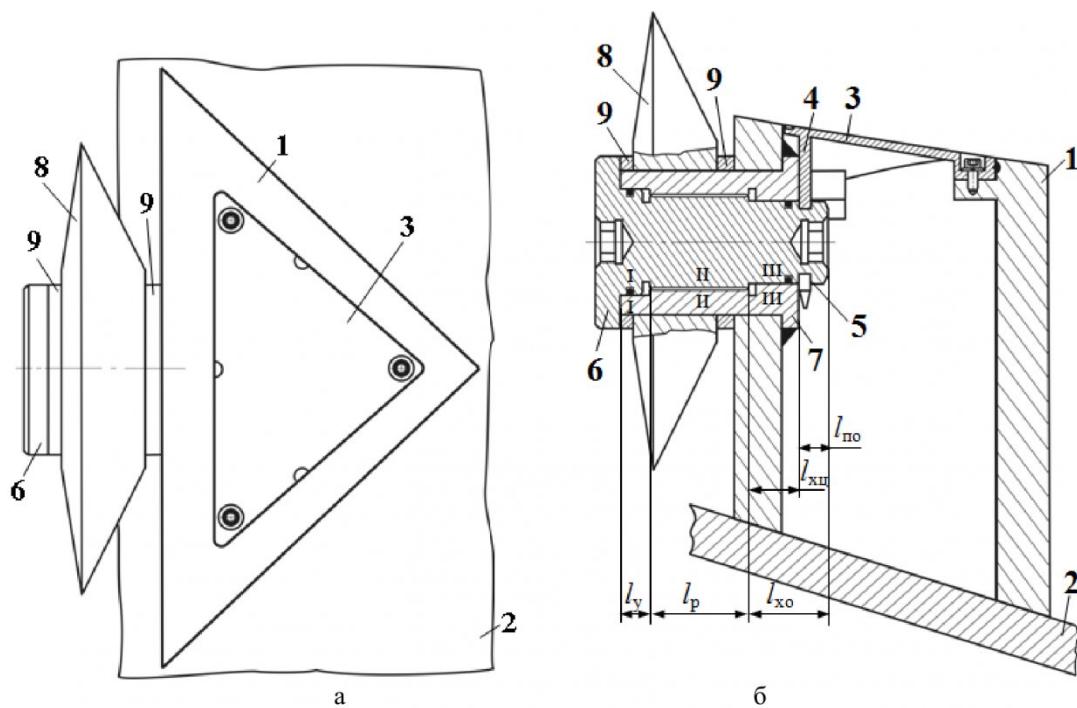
Устройство трехгранной призмы с узлом крепления дискового инструмента:
